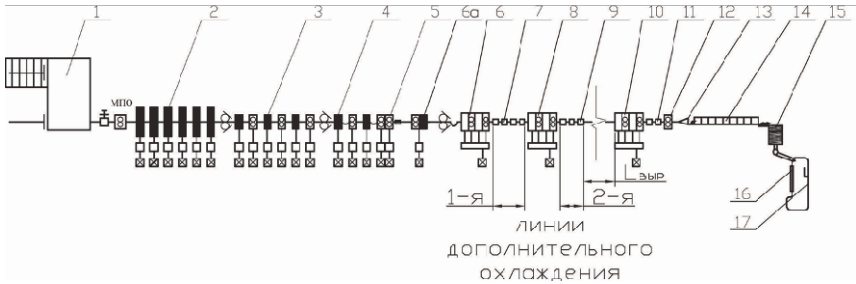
Перспективная схема высокоскоростного проволочного стана нового поколения для прокатки катанки широкого размерного и марочного сортамента
